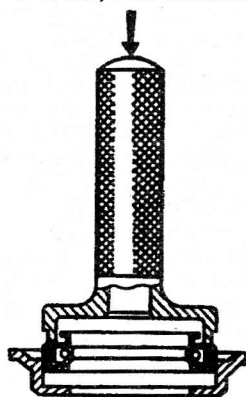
Запрессовка сальника в крышку распределительных шестерен оправкой 5-У-27733
